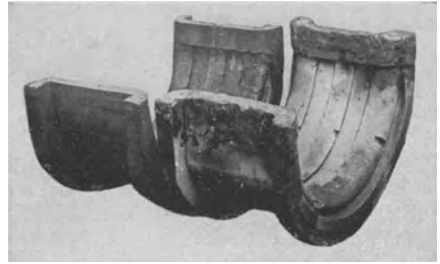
Durch Schweißung ausgebesserte Bronze-lagerschalen.
